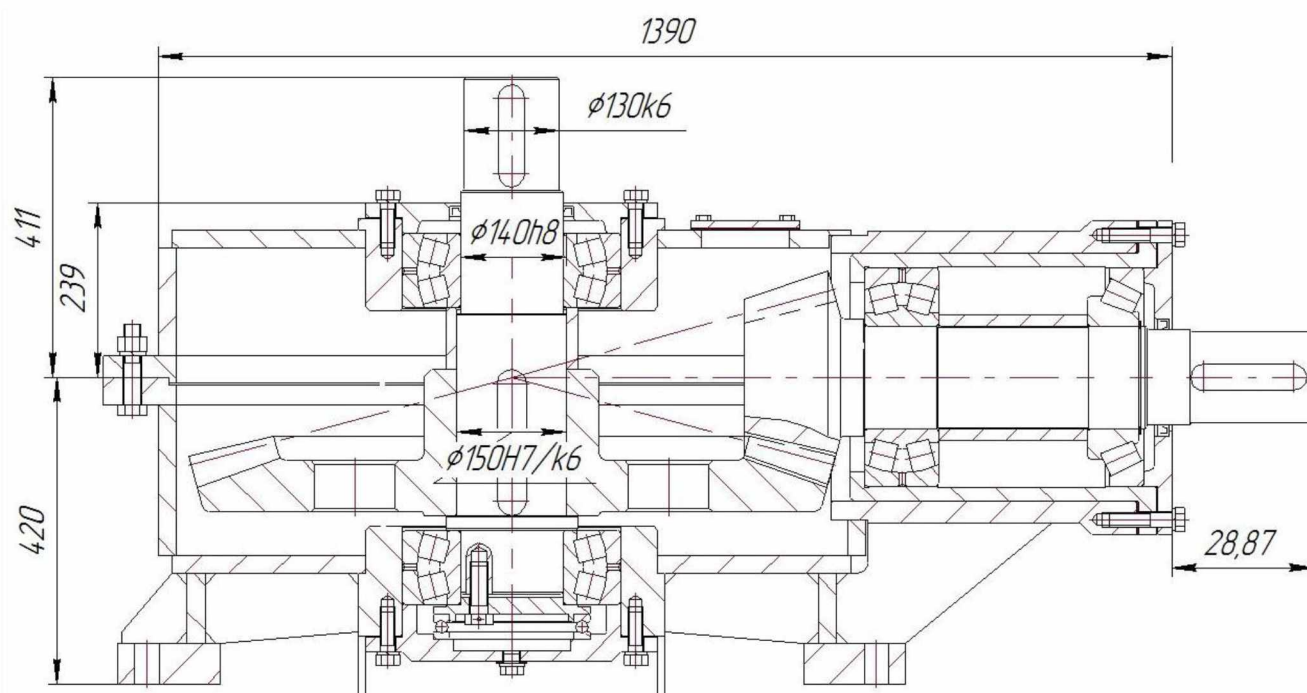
Редуктор механізму подрібнення ливарних сумішей
